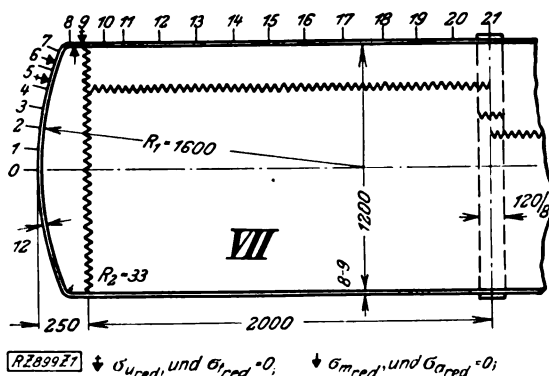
Elektrisch geschweißter Hohlkörper, Böden mit korbbogenförmigem Meridian.
